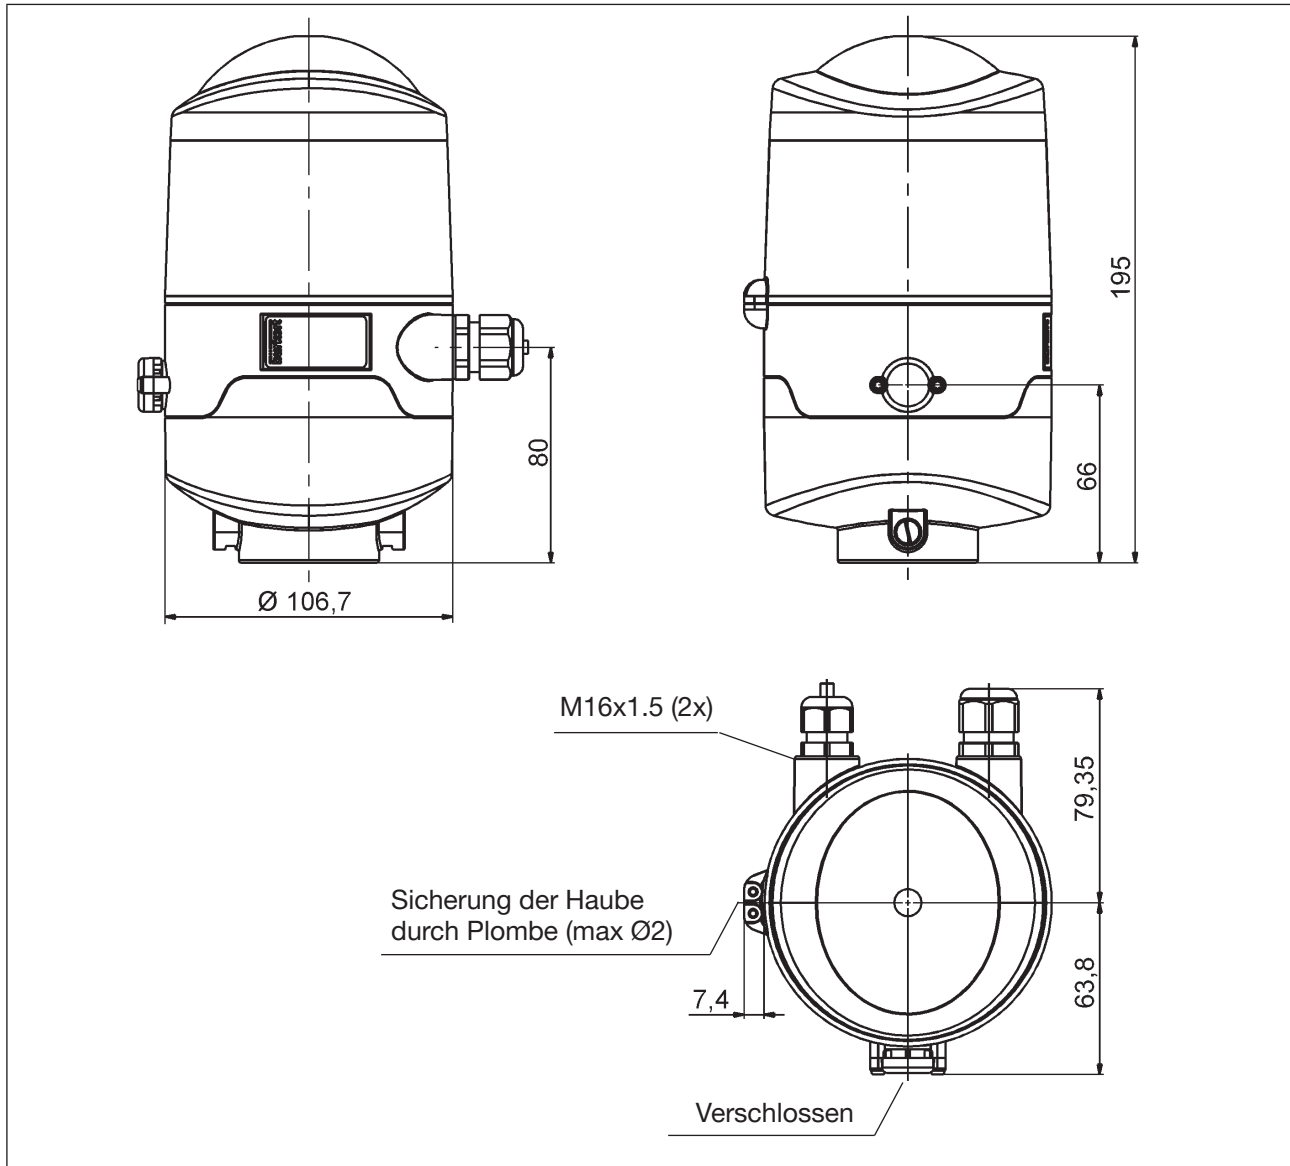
Maßzeichnung (für Varianten ohne Magnetventile = Rückmelder)
